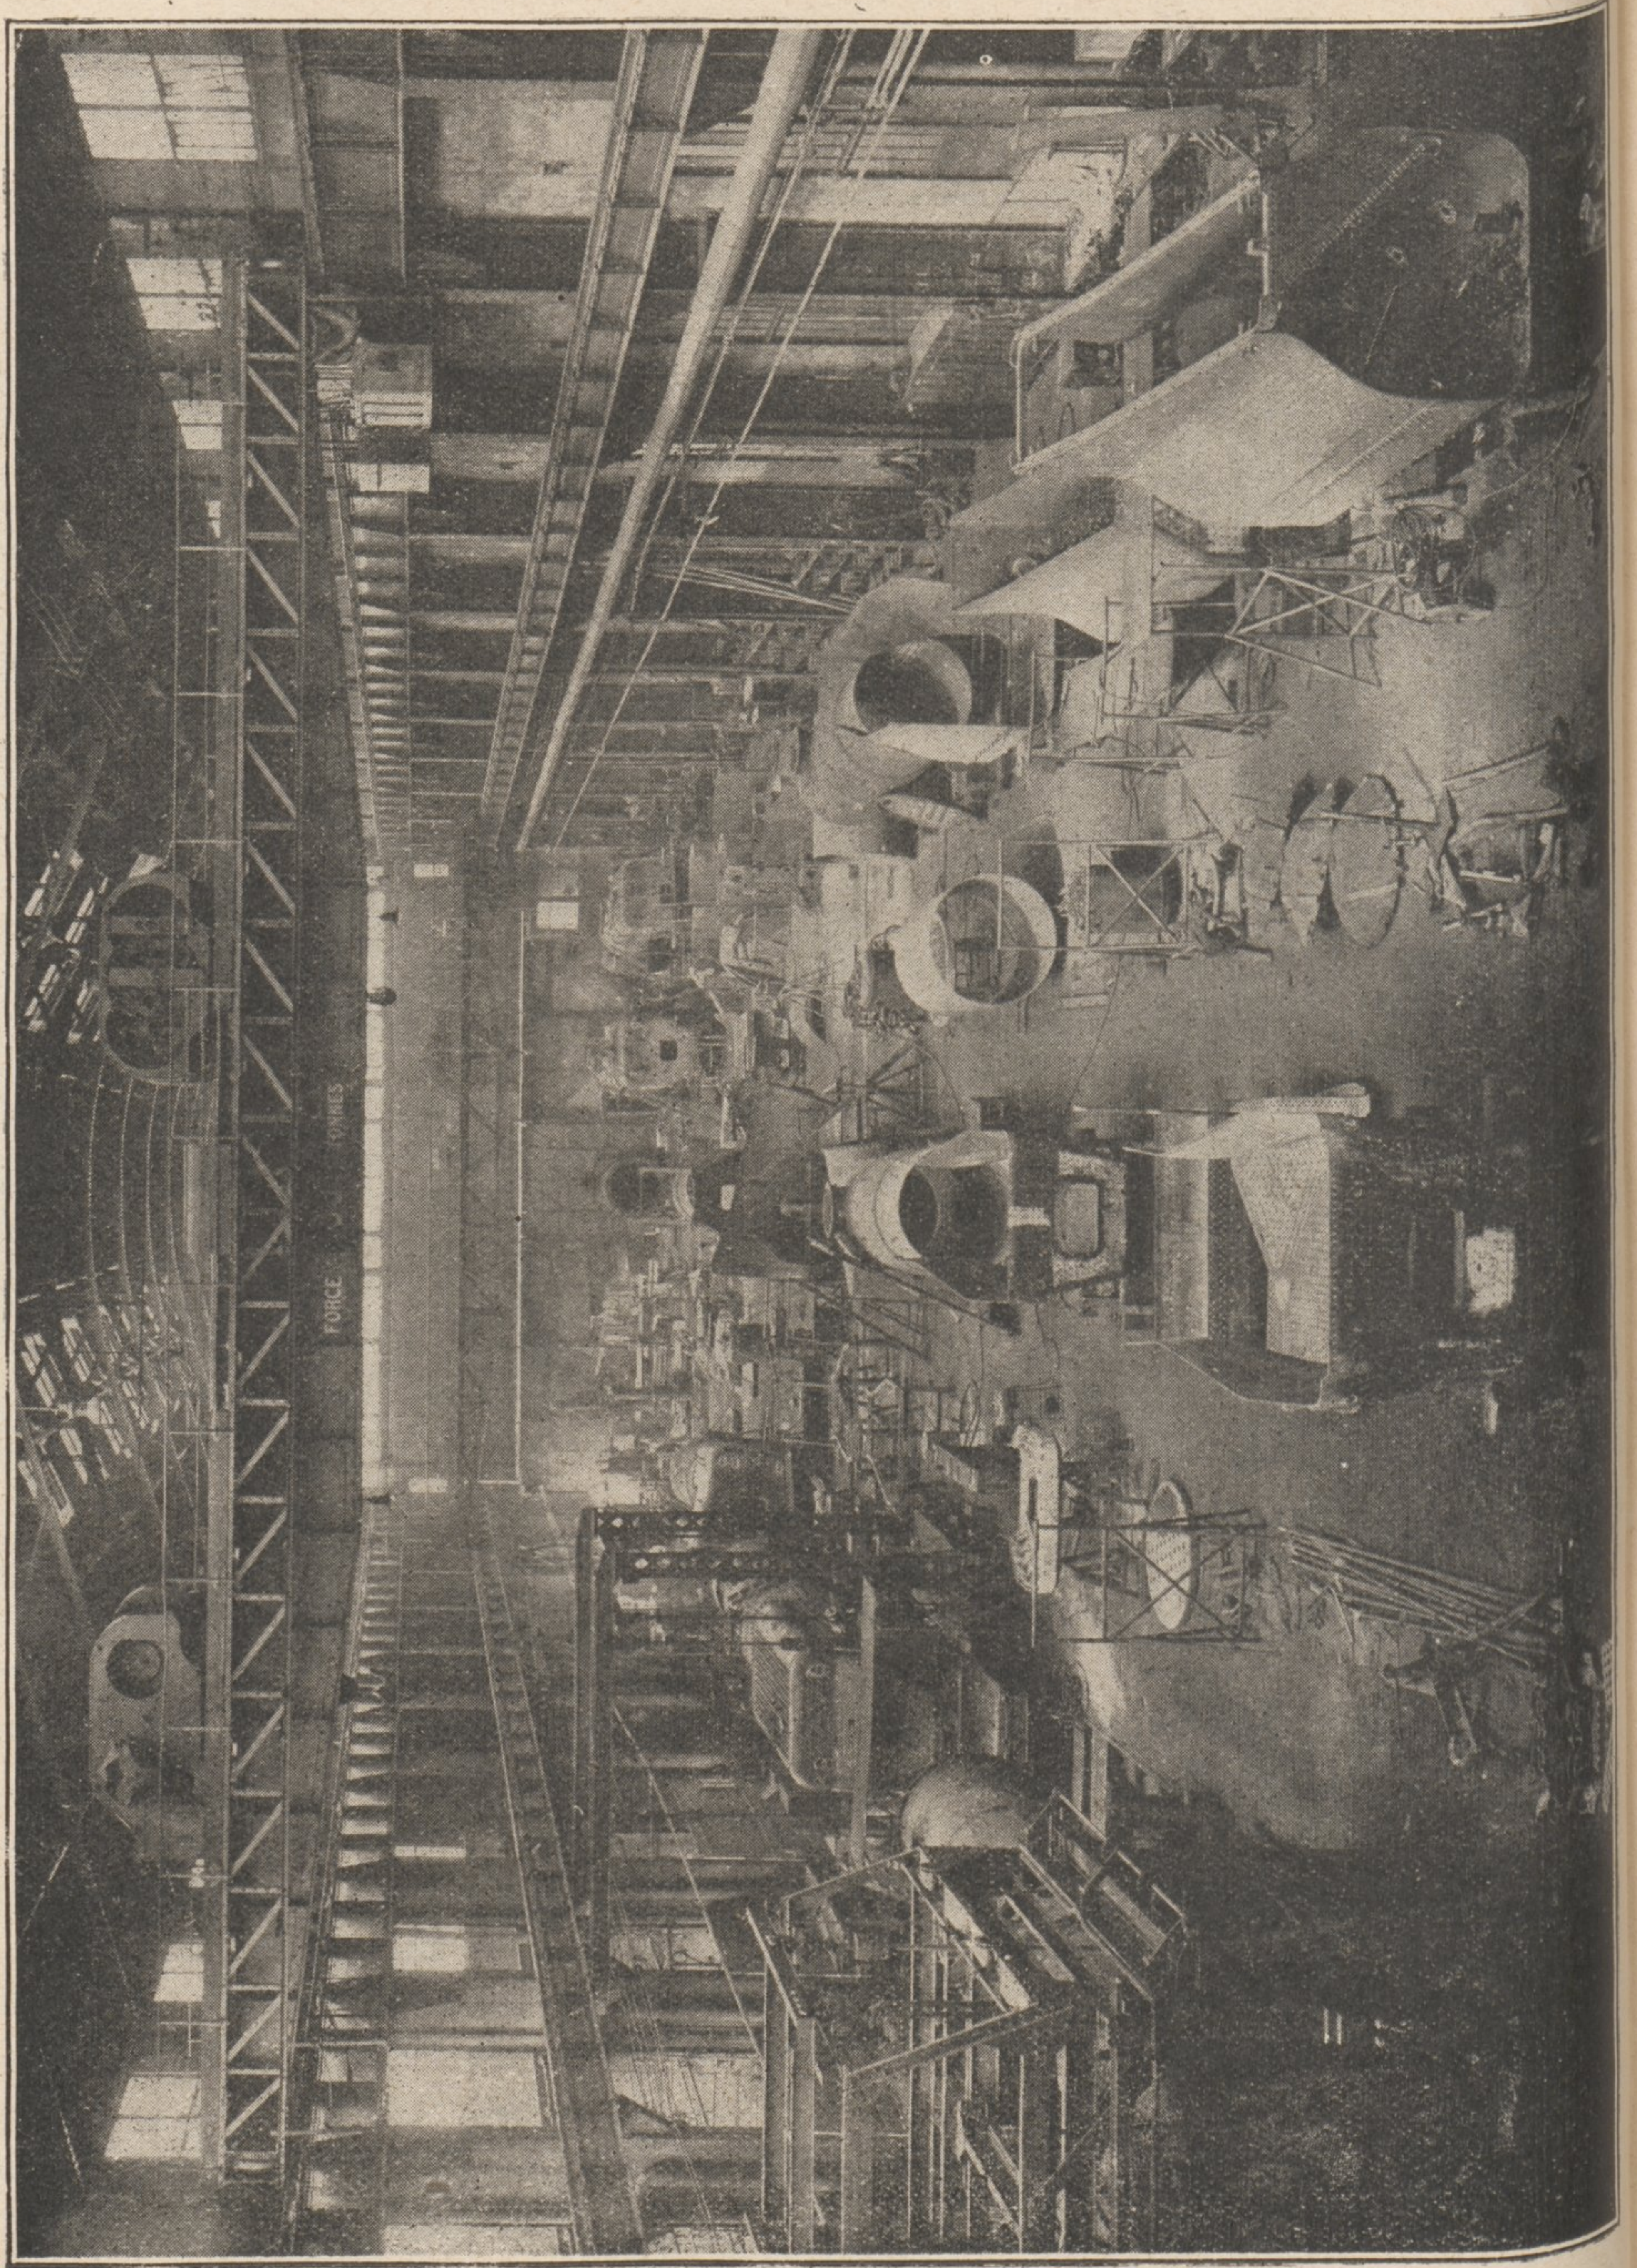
VUE D'ENSEMBLE DE LA CHAÎNE DE MONTAGE DES LOCOMOTIVES 4700
